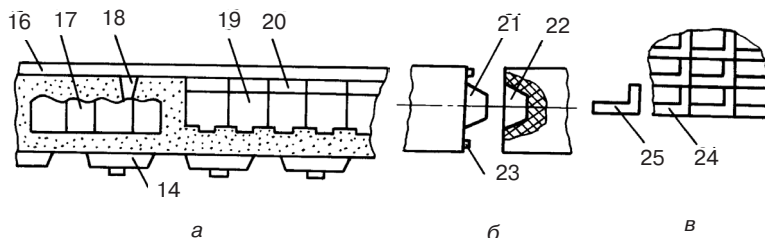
Примеры выполнения: а – формовки различных моделей; б – конструкций знаков-фиксаторов; в – сборки модели для непрерывного получения решетчатой отливки
